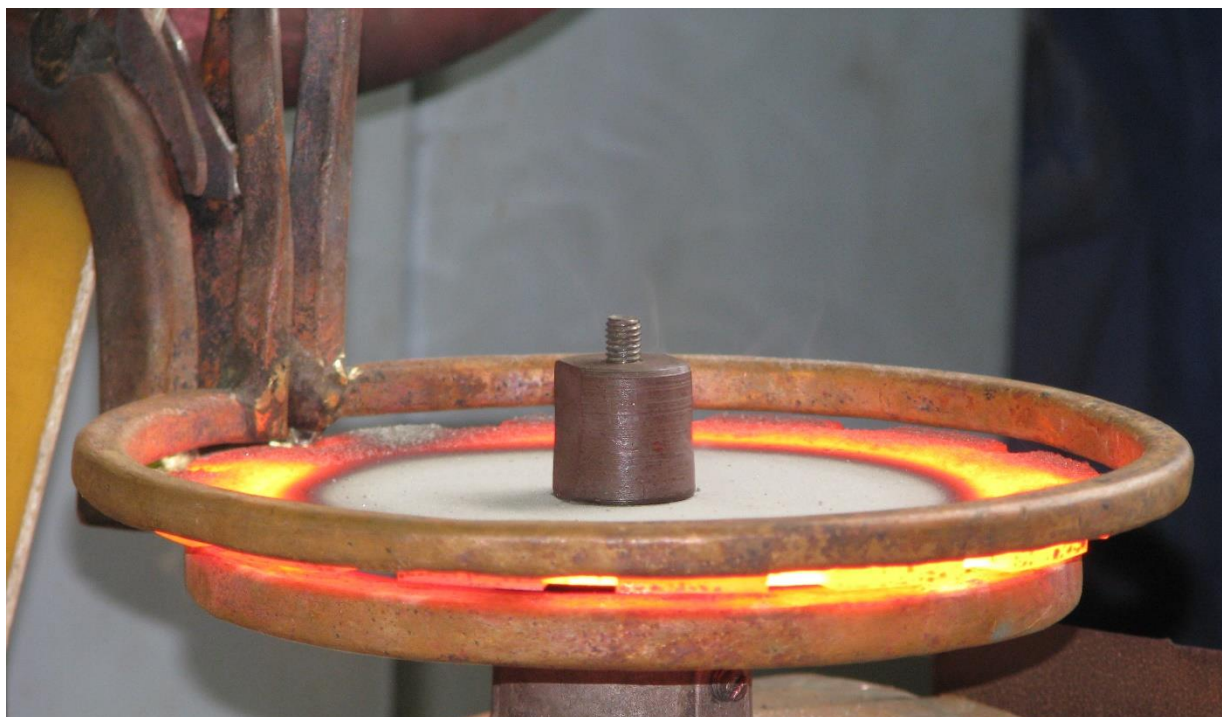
Процес одночасного індукційного наплавлення по всі робочій поверхні
